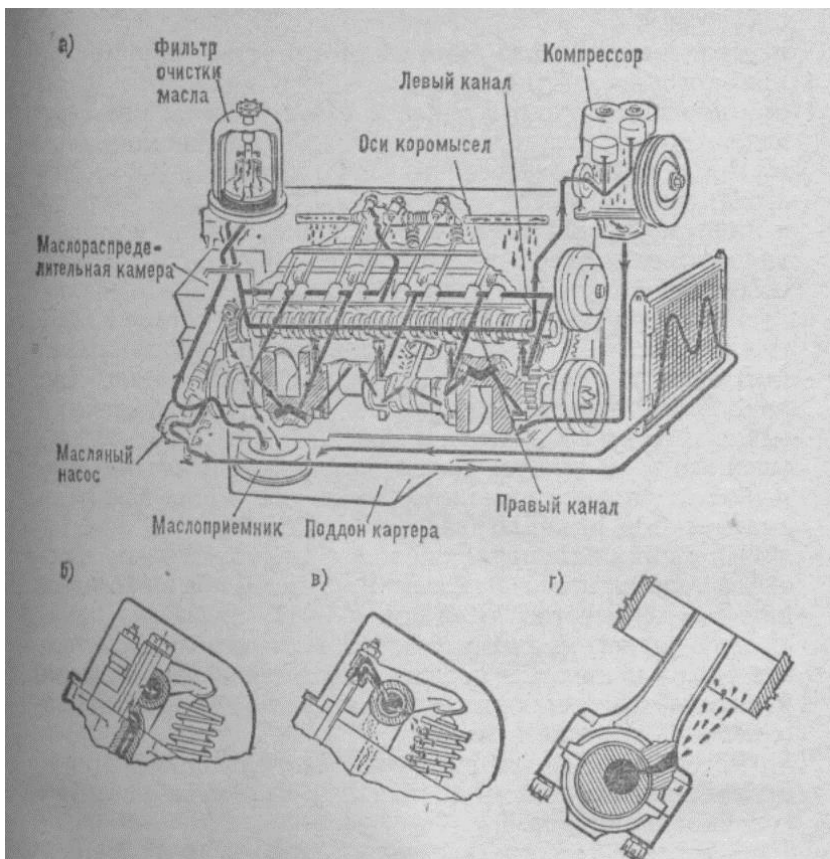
Система смазки двигателя ЗИЛ-130:
